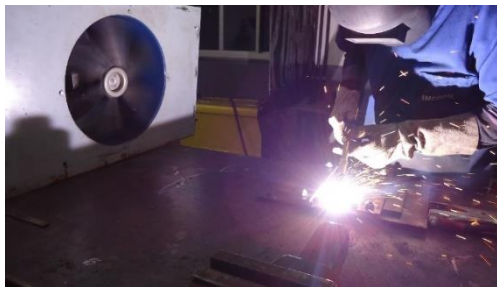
Sistema de soldagem. Corrente de ar agindo no sentido transversal ao sentido de soldagem.
